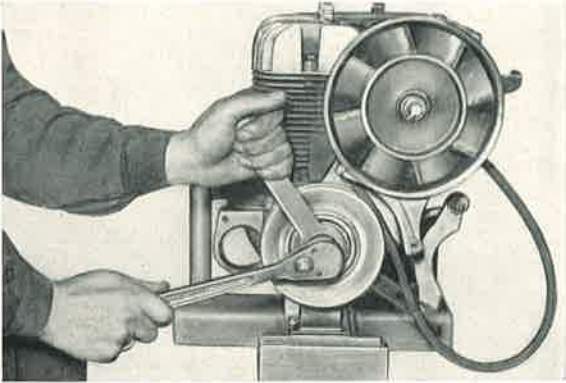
Beim Lösen der Mutter für Riemenscheibe wird mit Halteschlüssel für Riemenscheibe gegengehalten.
